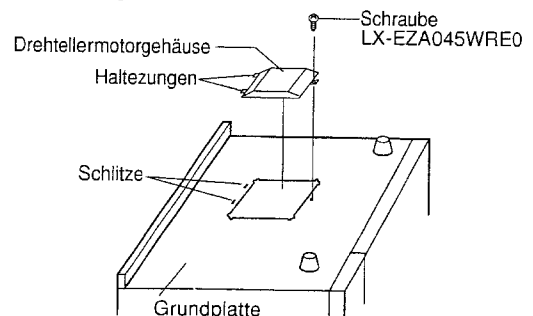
(b). Wiedereinbau des Drehtellermotorgehäuses
